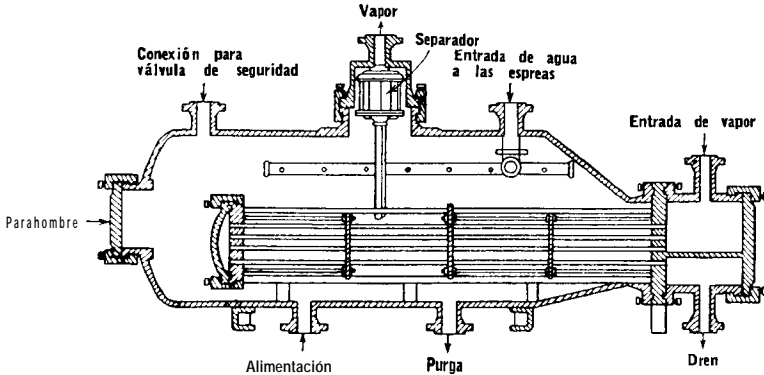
Evaporador para planta de fuerza. (Alco Products)
